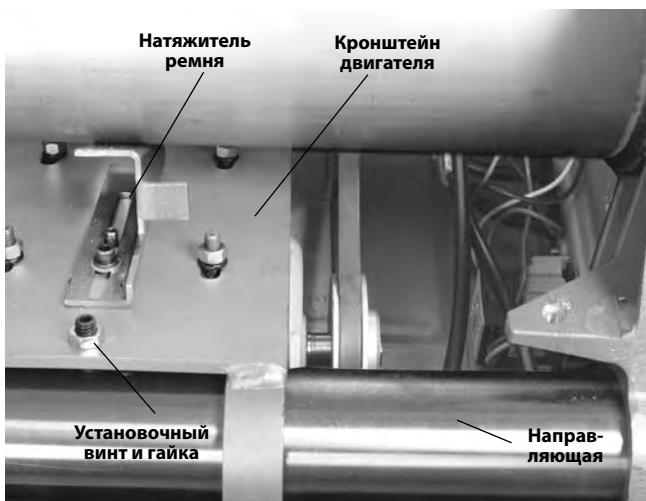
Кронштейн двигателя и натяжитель ремня
